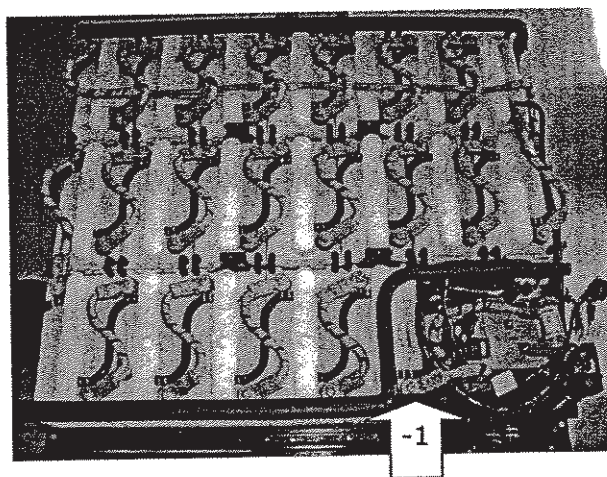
Ny HV boks (versjon E) komplett med nye kabler.
